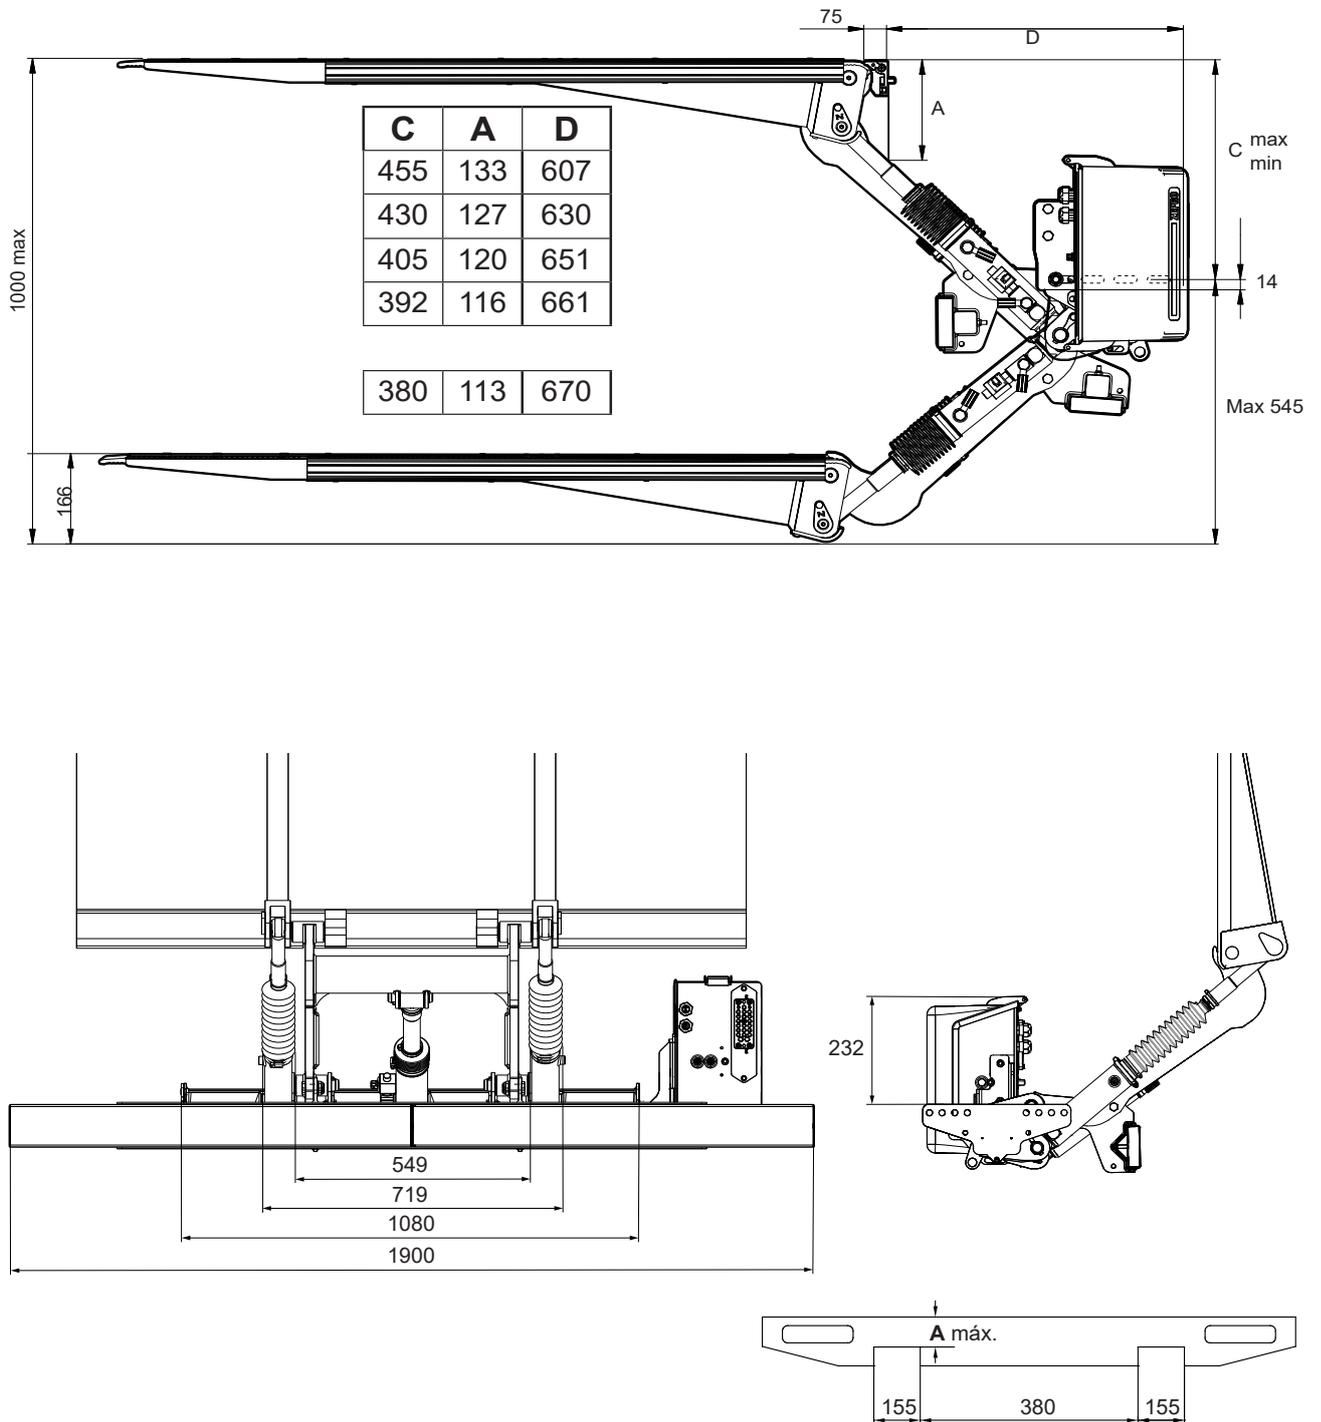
Dimensiones de montaje para Z3NW(U) 75-100
